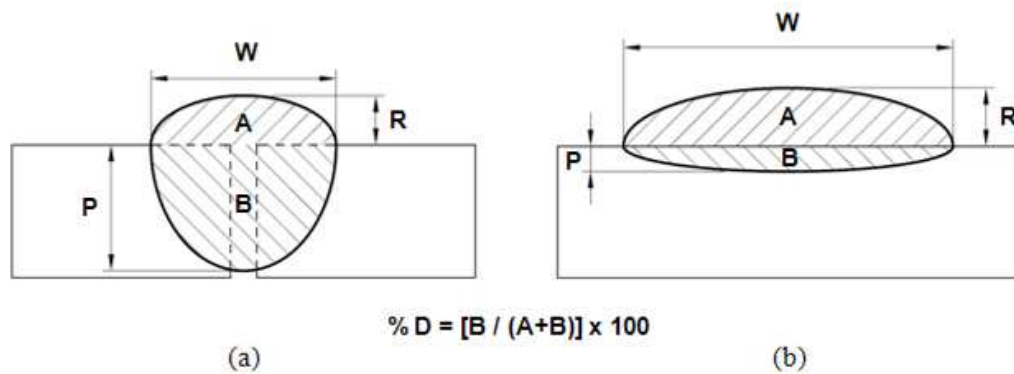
Perfil geométrico desejado do cordão de solda: a) união da junta soldada (aplicações convencionais); b) soldagem de revestimento
